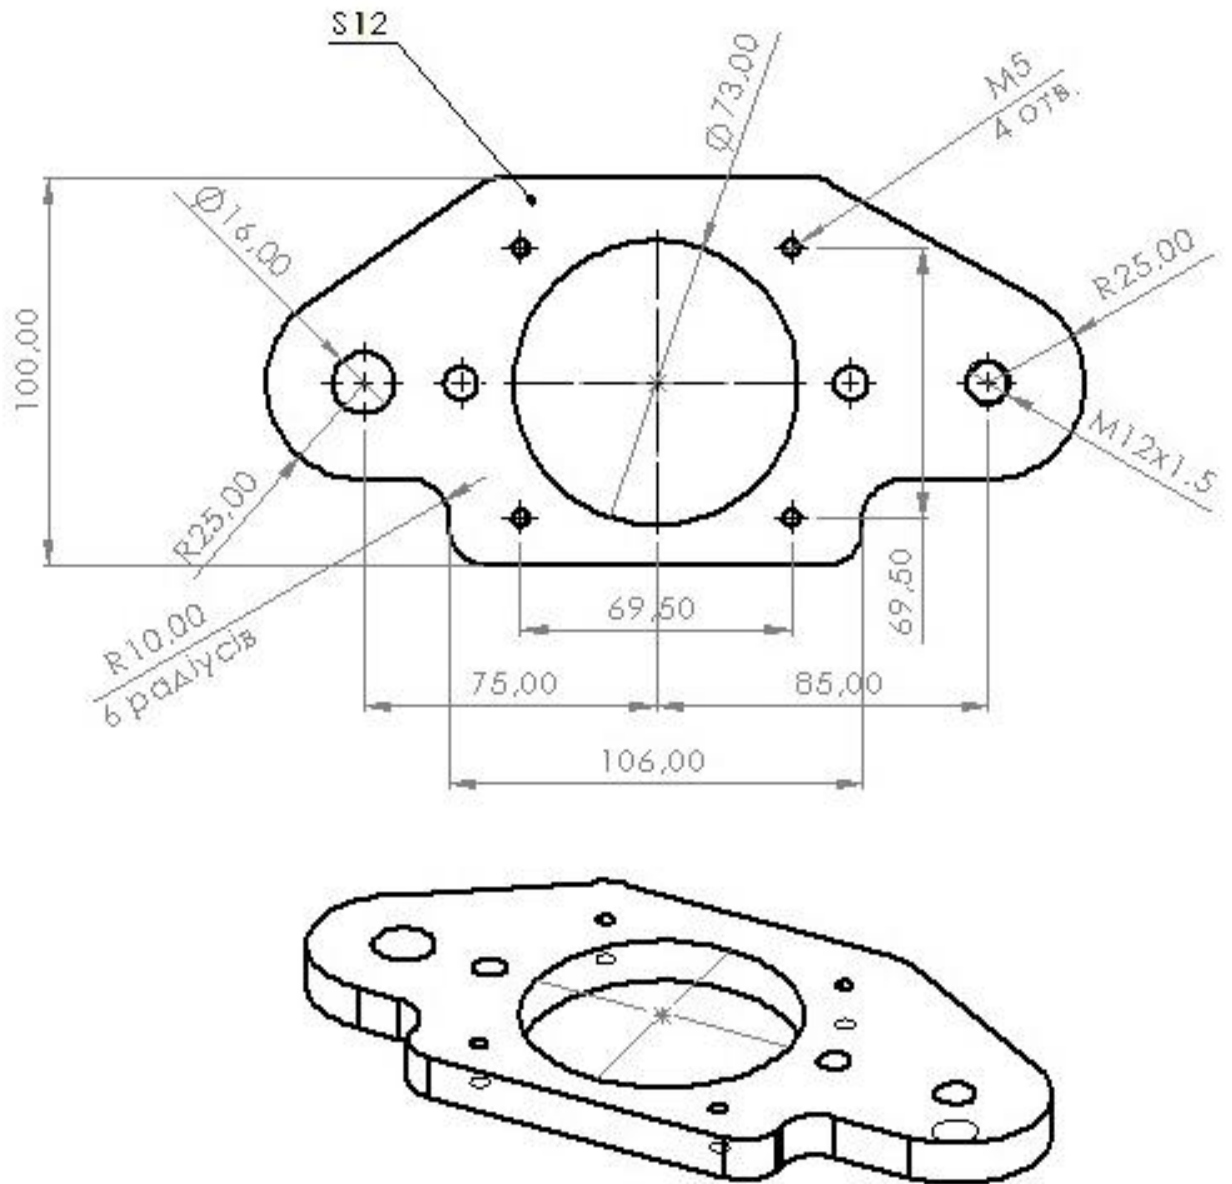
Креслення деталі «Куліса двигуна катерки Y»
